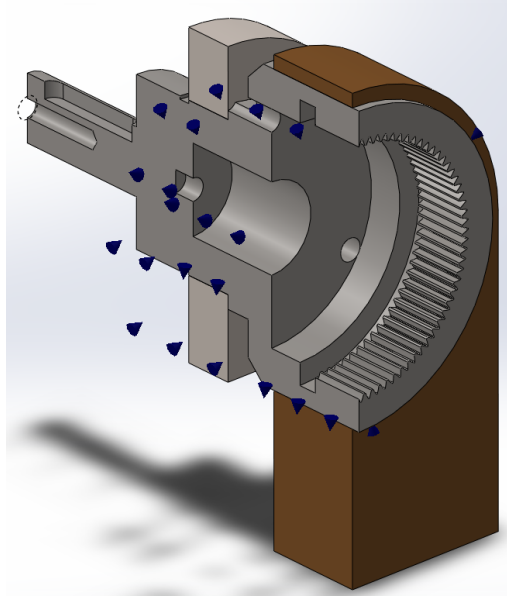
Conexiones de rodamiento entre rodamiento-árbol y casquillo-árbol.
